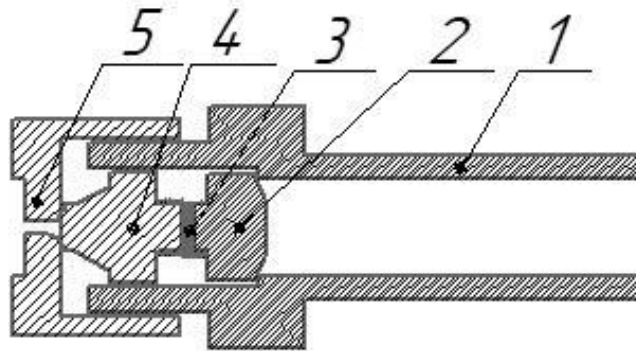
Будова форсунки, схематичне зображення: 1 – корпус;
